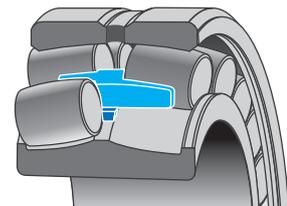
ULTAGE-Ausführung für große Wälzlager
